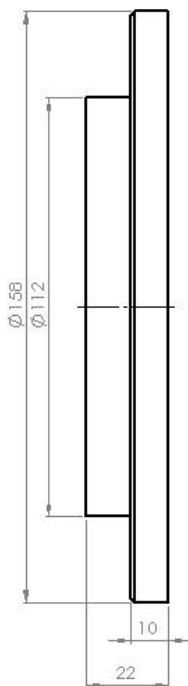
Flange do Acoplamento Antes da Usinagem
